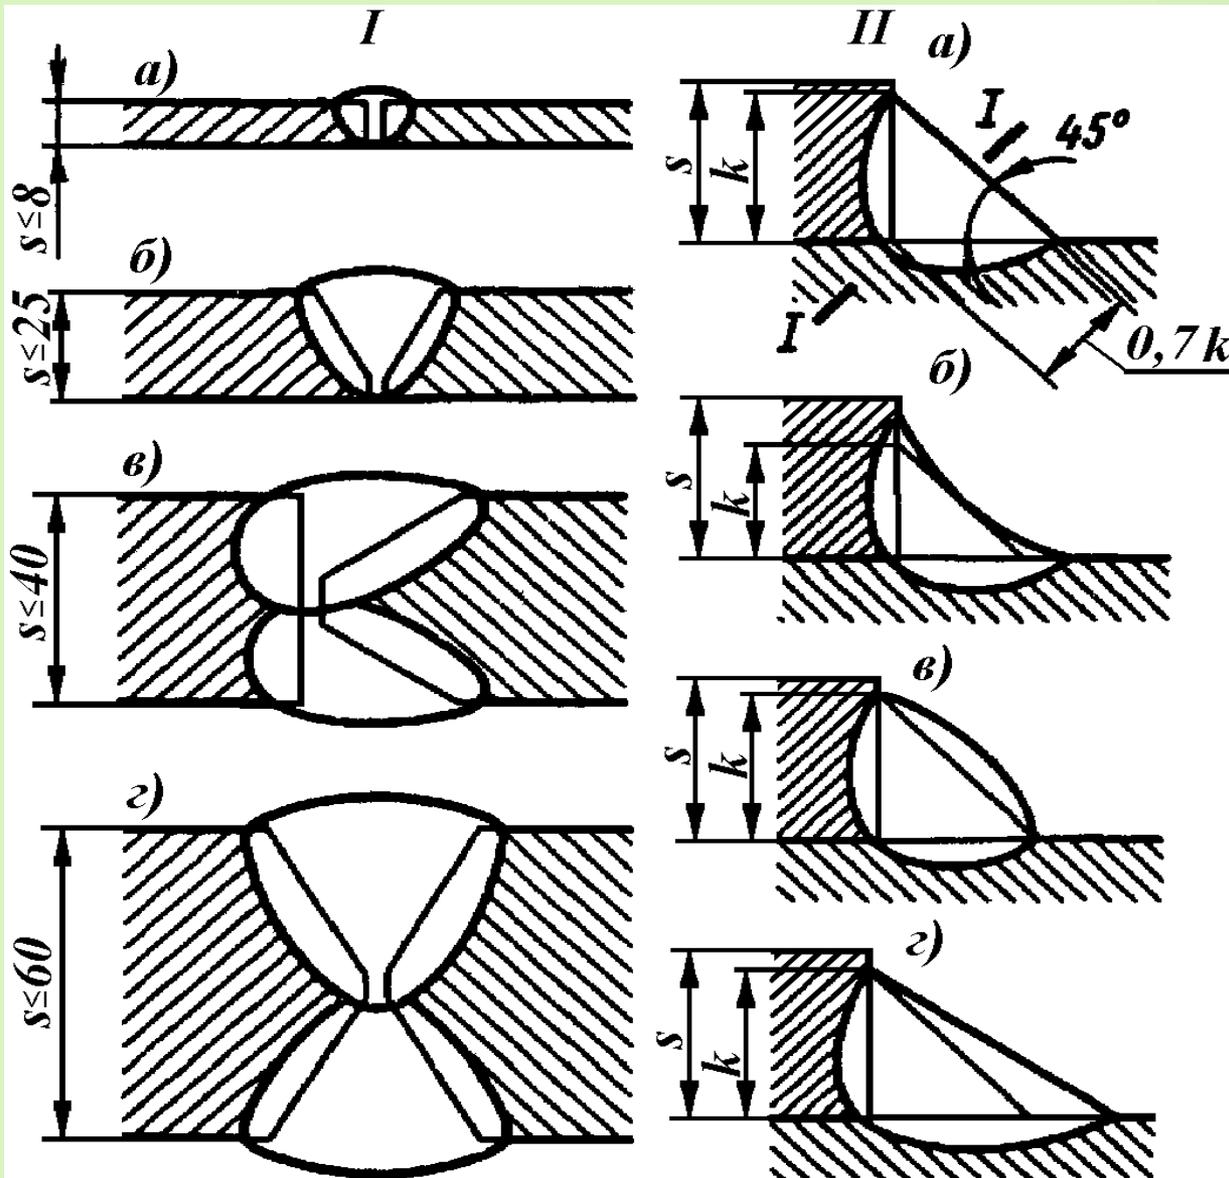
Конструктивные типы сварных соединений:
